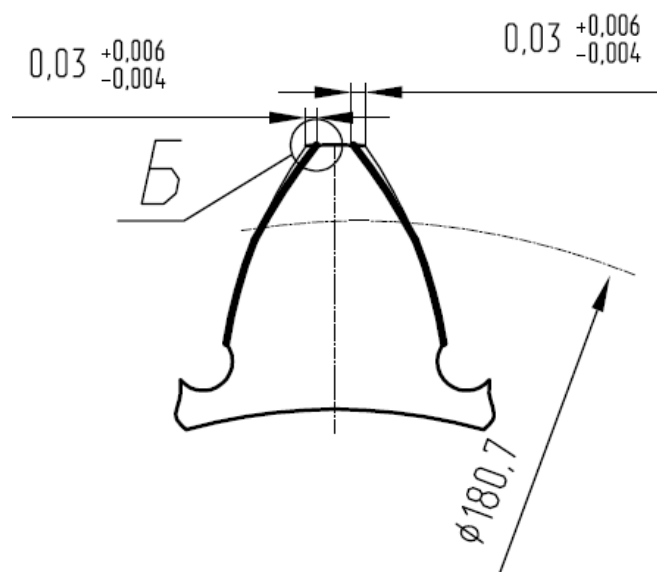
Модификации профиля зуба цилиндрического зубчатого колеса
